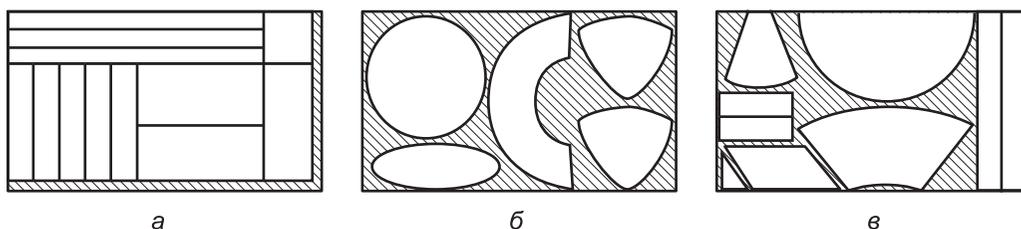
Раскрой тонколистового металла: а – прямолинейный; б – криволинейный; в – смешанный (заштрихованы отходы металла)
